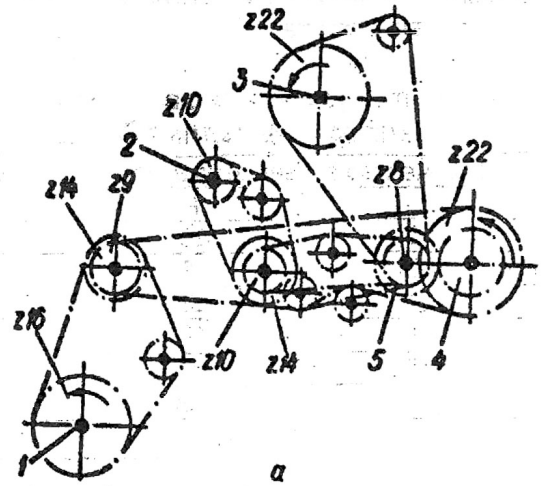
Схема передаточного механизма сеялки СЗ-3,6А с коробкой передач:
